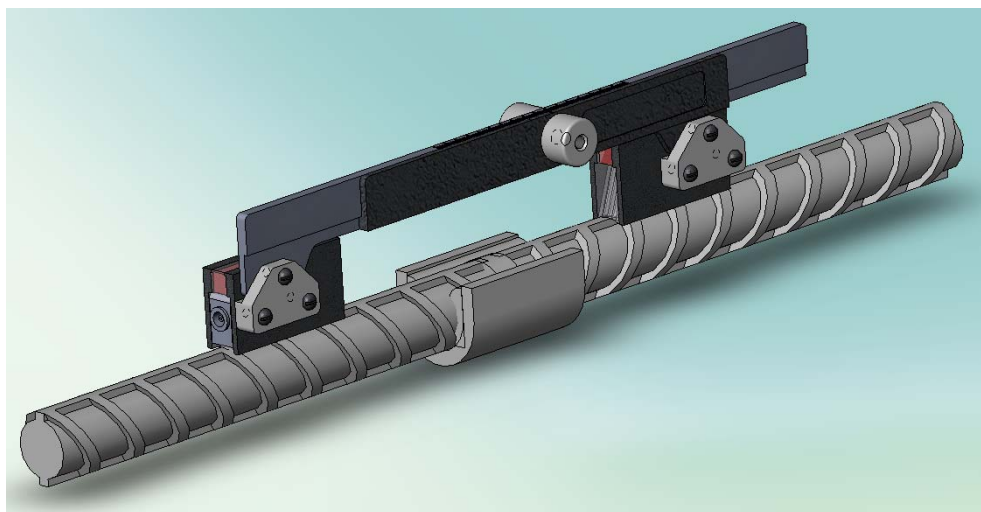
Комбинированный ультразвуковой преобразователь для контроля сварных швов арматуры ПА123-1,8-65⁰. Внешний вид.
